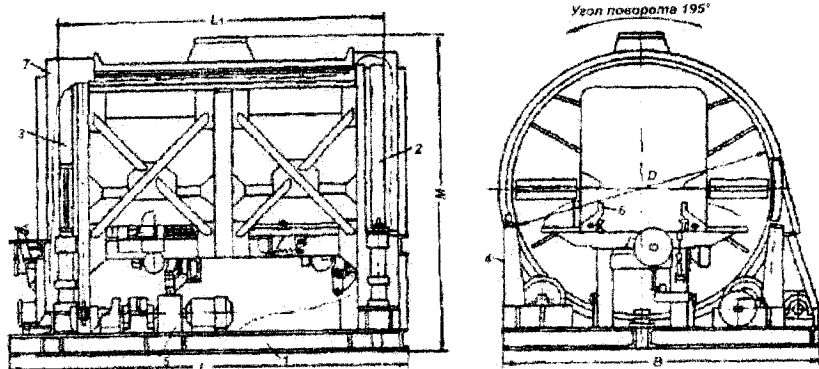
Круговой опрокидыватель типа ОК:
